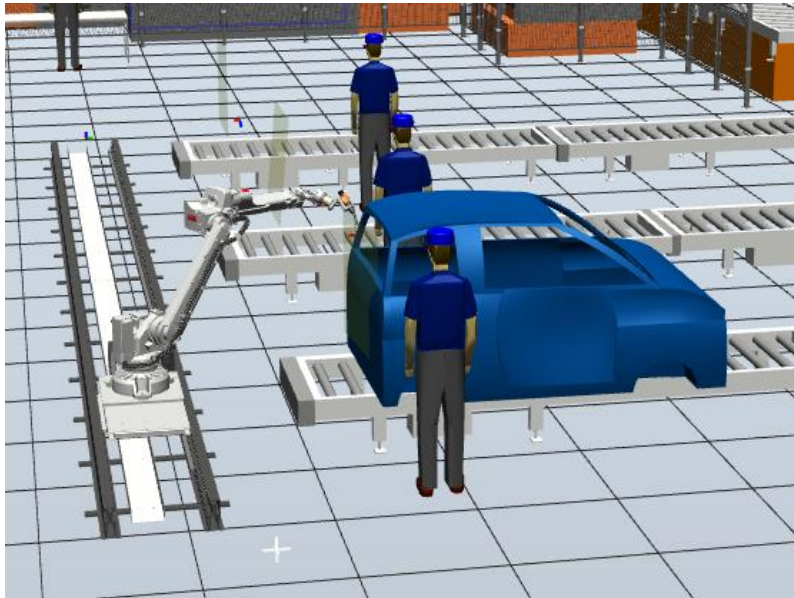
Proceso de soldadura de la parte trasera del chasis en la cuarta etapa.
